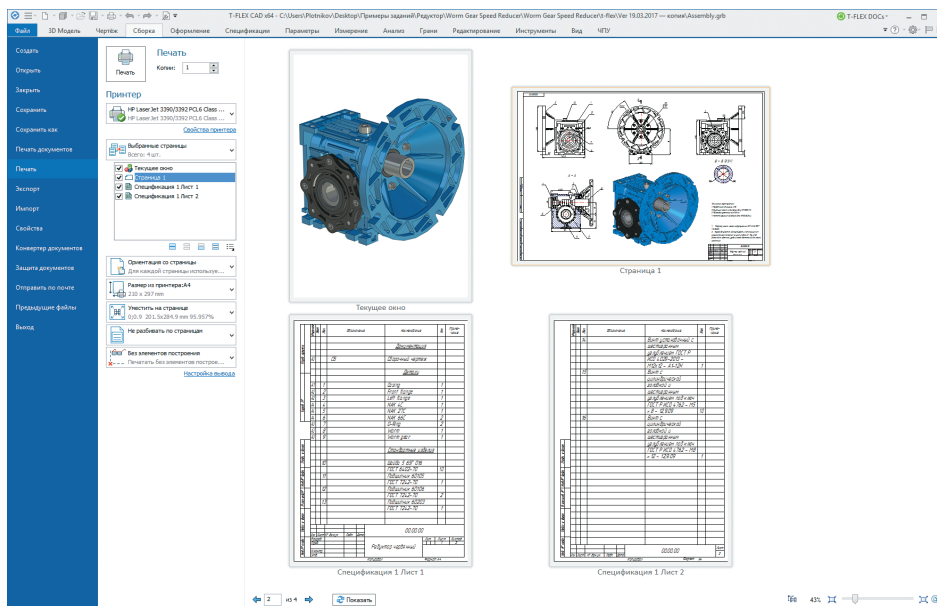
Печать нескольких страниц разных типов, включая 3D-вид
